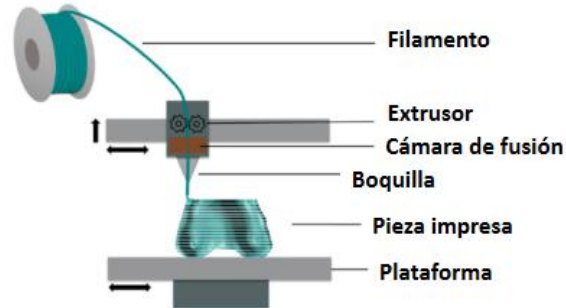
Proceso de impresión 3D con Fused Filament Fabrication. Adaptada de [54].
